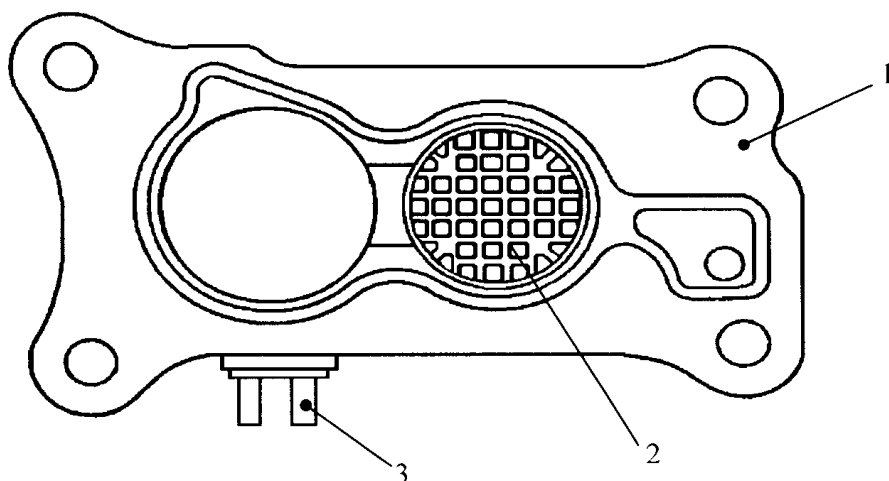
Подогреватель сотовой конструкции, монтируемый в прокладке под блоком топливоподачи: 1 – прокладка; 2 – сотовый нагревательный элемент; 3 – токопроводы
